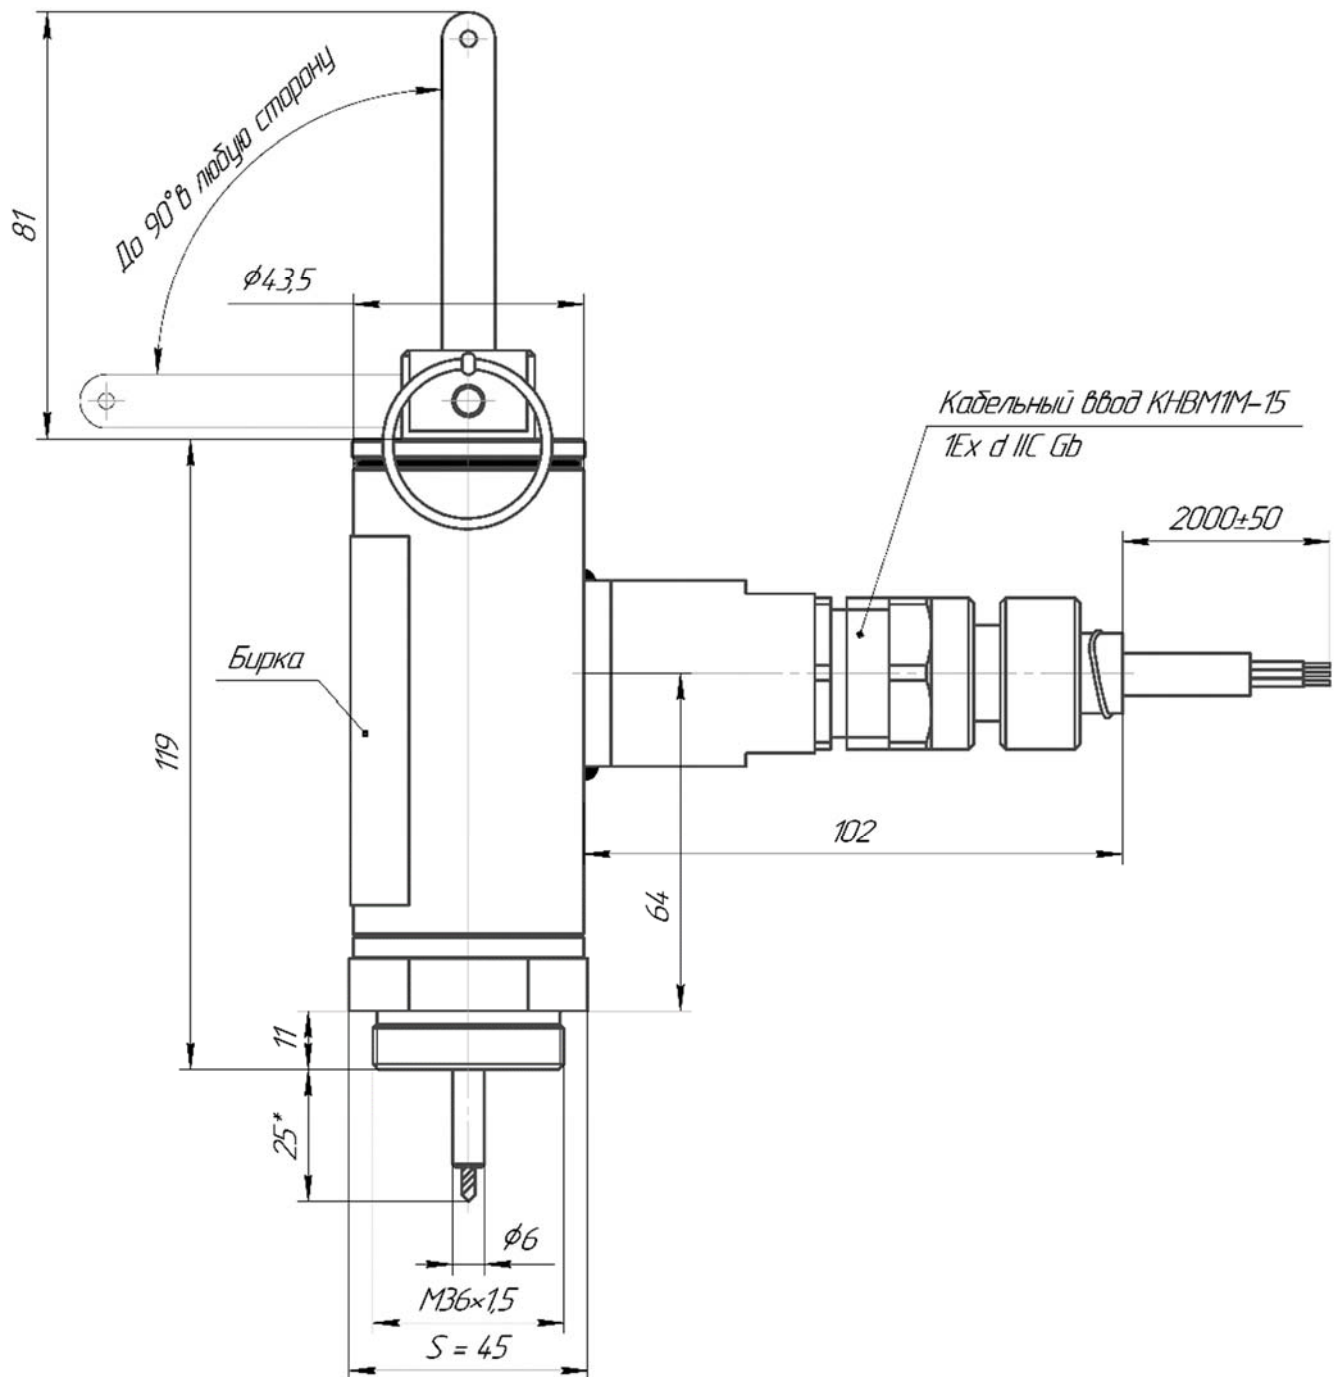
а – Габаритные, установочные и присоединительные размеры УП-150ЭМ-Р(ВЗ).
